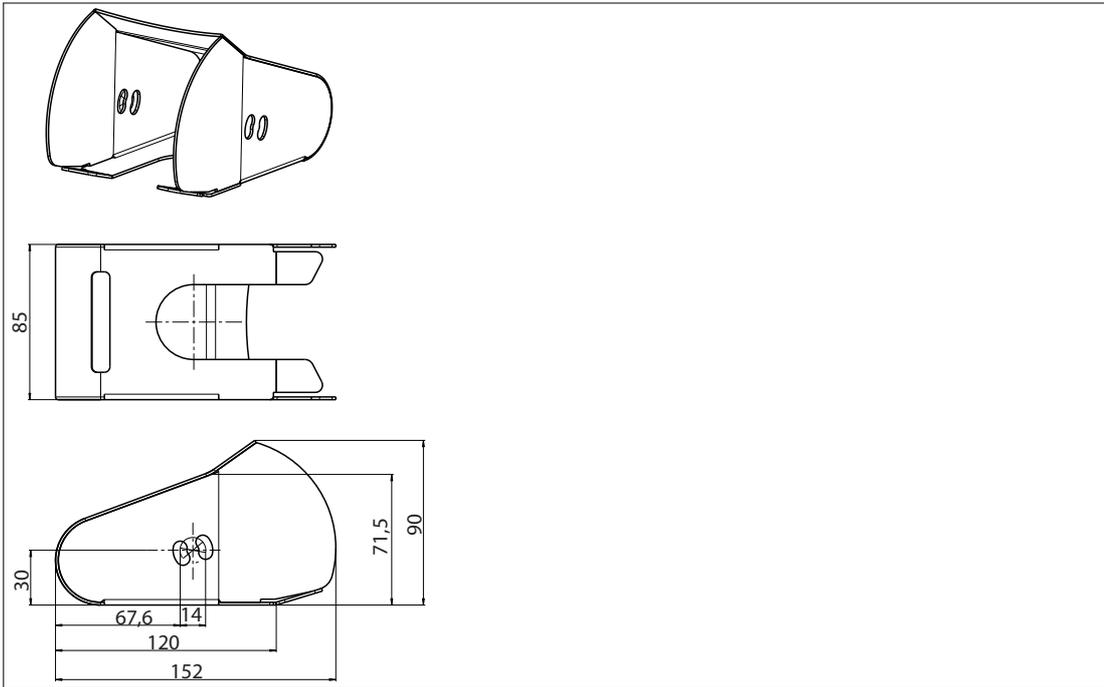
Abmessungen Halter für Barcode-Handheld
